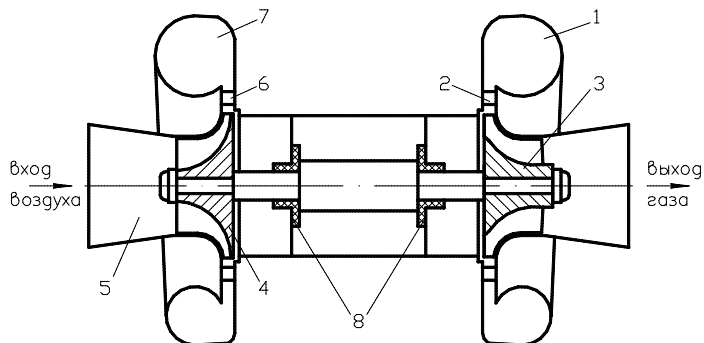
Турбокомпрессор: 1 – впускной тракт турбины; 2 – сопловой аппарат; 3 – рабочее колесо; 4 – колесо компрессора; 5 – входное устройство; 6 – диффузор; 7 – воздухосборник; 8 – подшипники скольжения.
